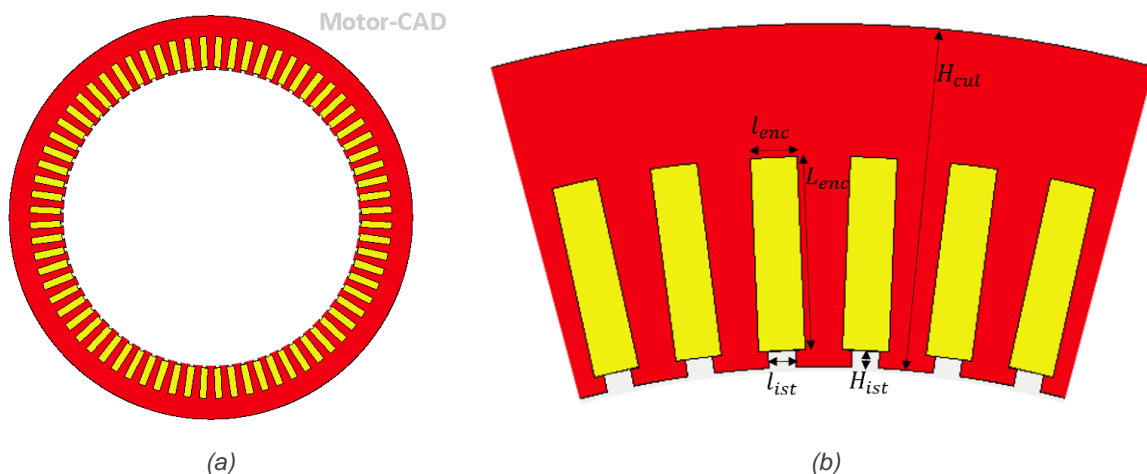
Géométrie du stator des deux machines synchronreluctantes : (a) stator complet et (b) un pôle du stator
